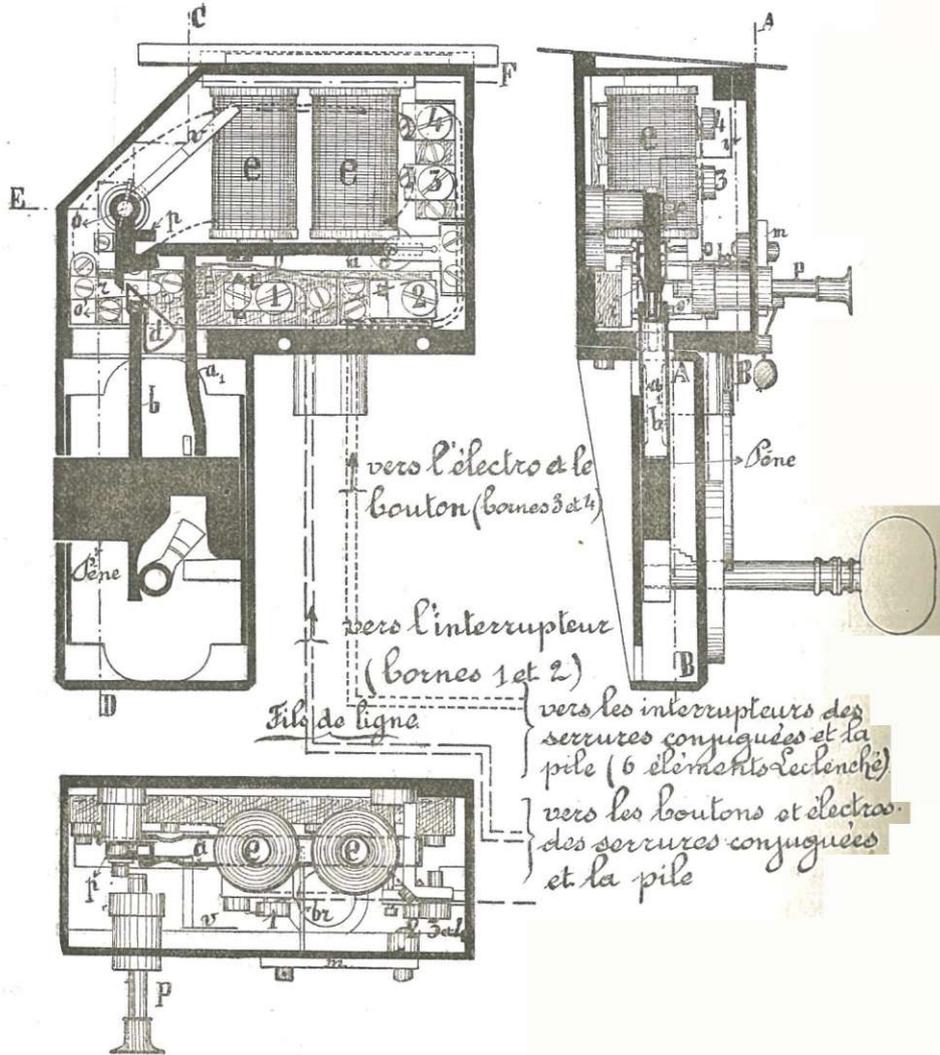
Vue supérieure suivant EF. Serrure ouverte.
